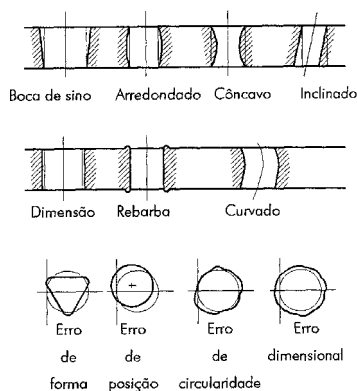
Desvios geométricos e dimensionais na furação [Tool and Manufacturing, 1983]
